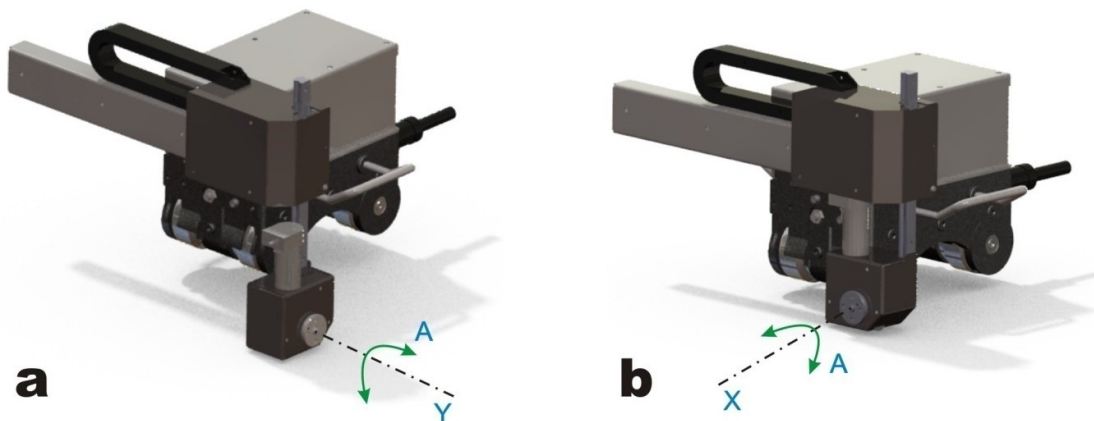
Primeiro protótipo do TARTÍLOPE V4. Em (a) concepção para soldagem de dutos e em (b) para soldagem de tubos de parede de caldeira
